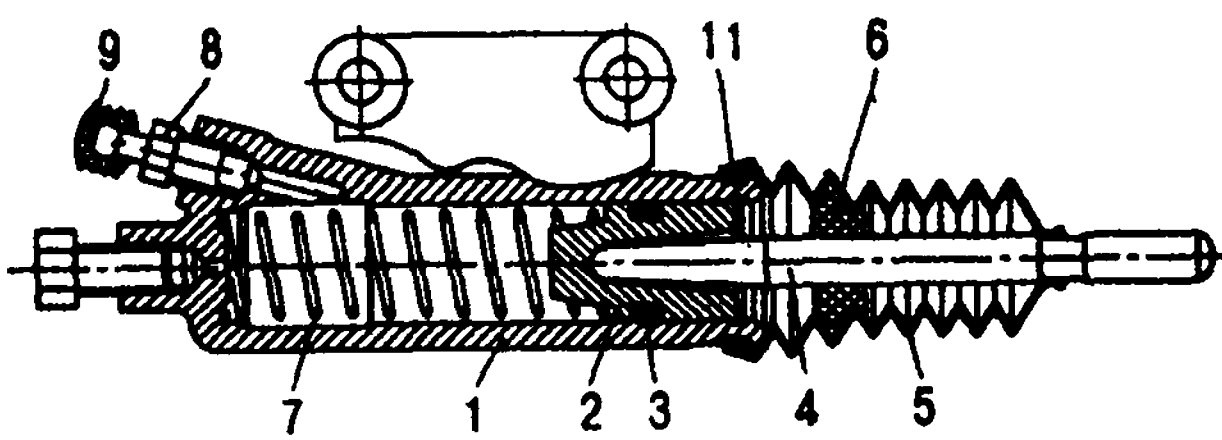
Рабочий цилиндр привода выключения сцепления: 1 - корпус цилиндра; 2 - поршень; 3 - манжета; 4 - толкатель; 5 - чехол; 6 - кольцо защитное; 7 - пружина; 8 - клапан перепускной; 9 - колпачок защитный; 11 - кольцо
